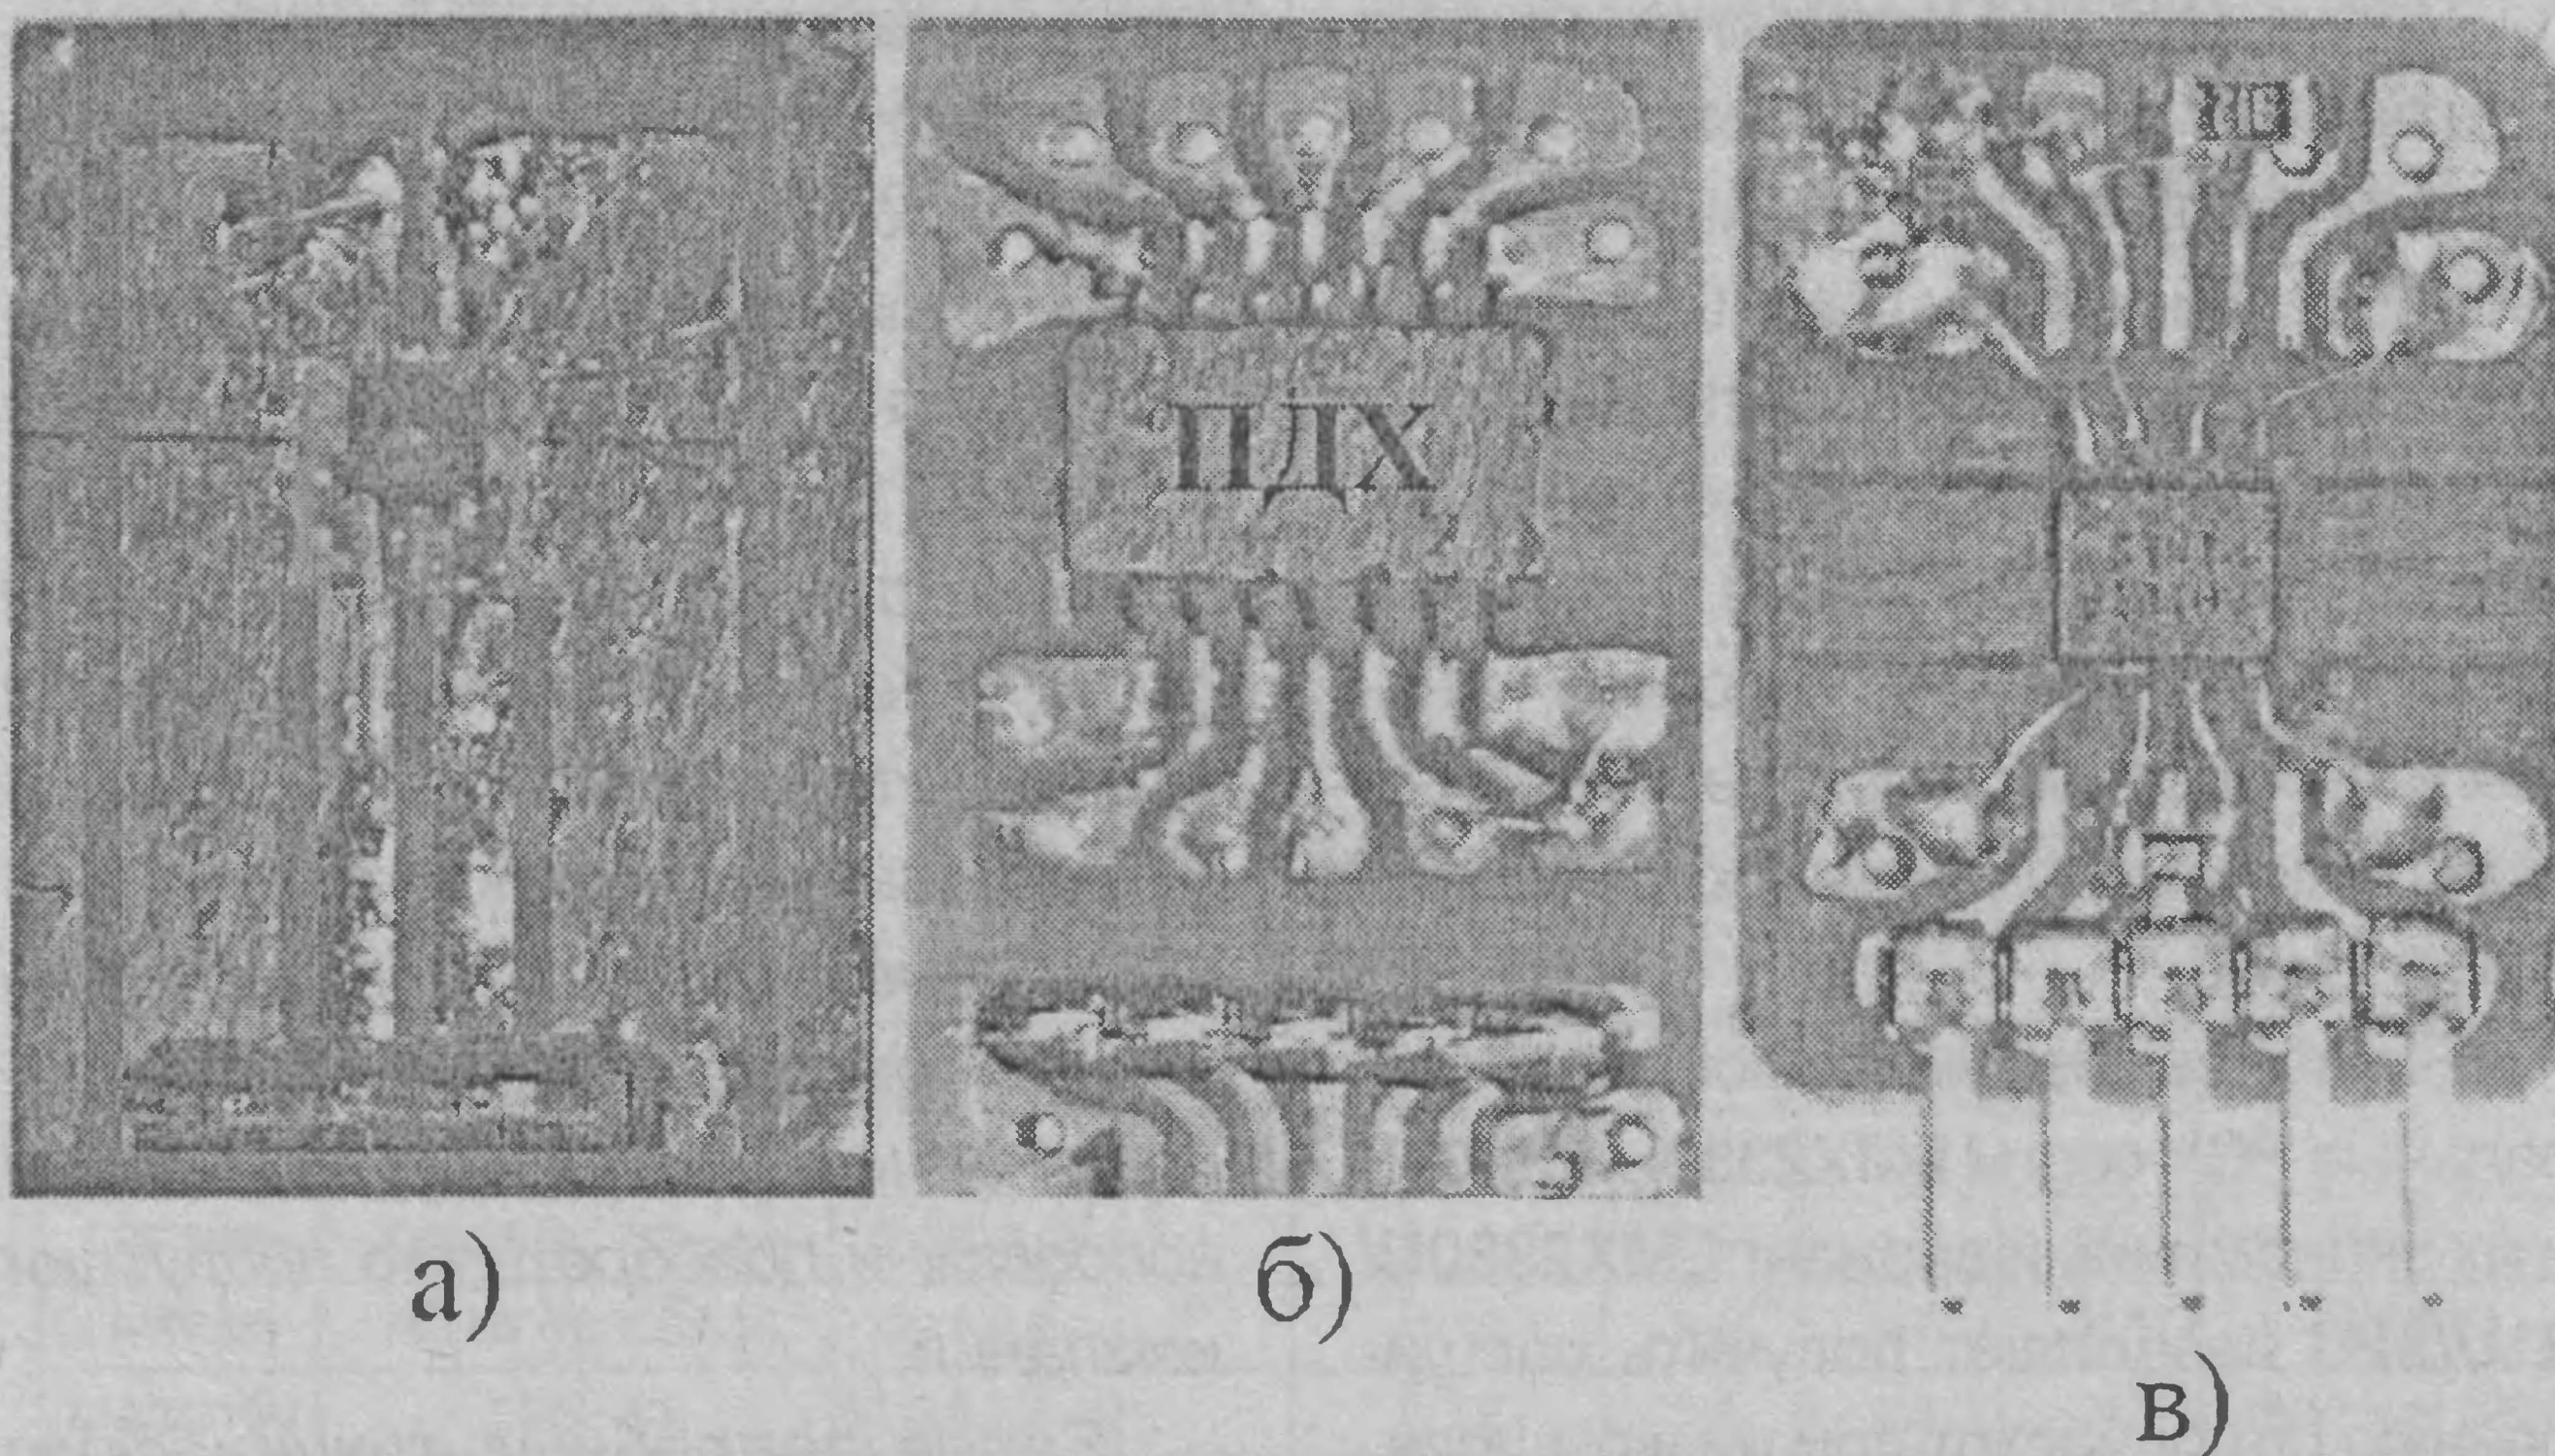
Внешний вид плат с различными ПМП: а - с бескорпусным датчиком Холла типа ПХИ; б - с ПДХ в корпусе 401.14-3; в - с магниточувствительной ИС типа AD22151
